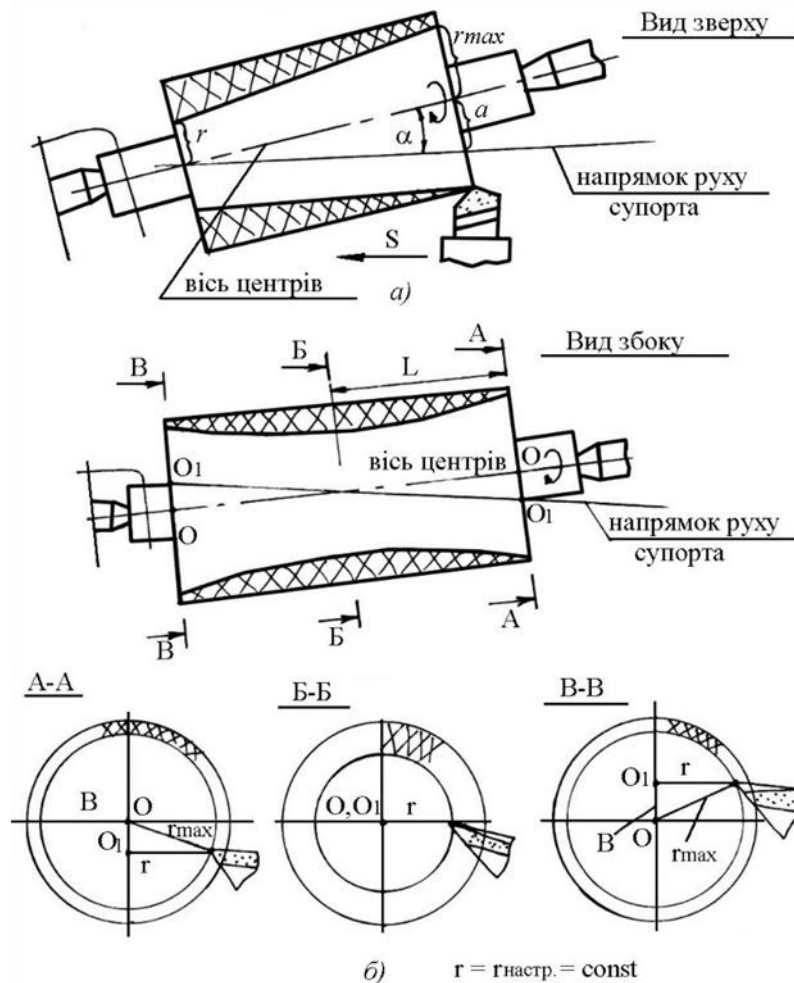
Похибки форми при обточуванні циліндричних заготовок
